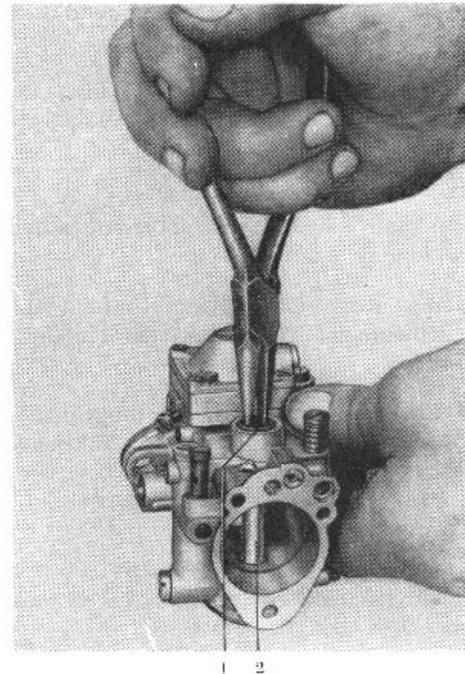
Einsatzstück mit Tauchrohr ausbauen
